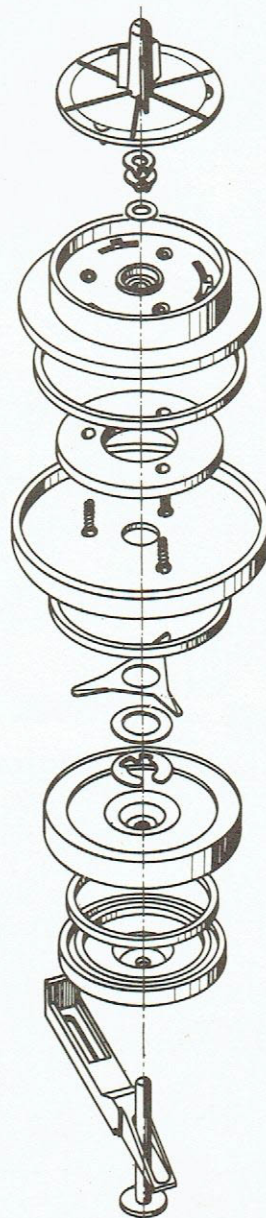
Vue éclatée de l'assiette bobineuse de droite
